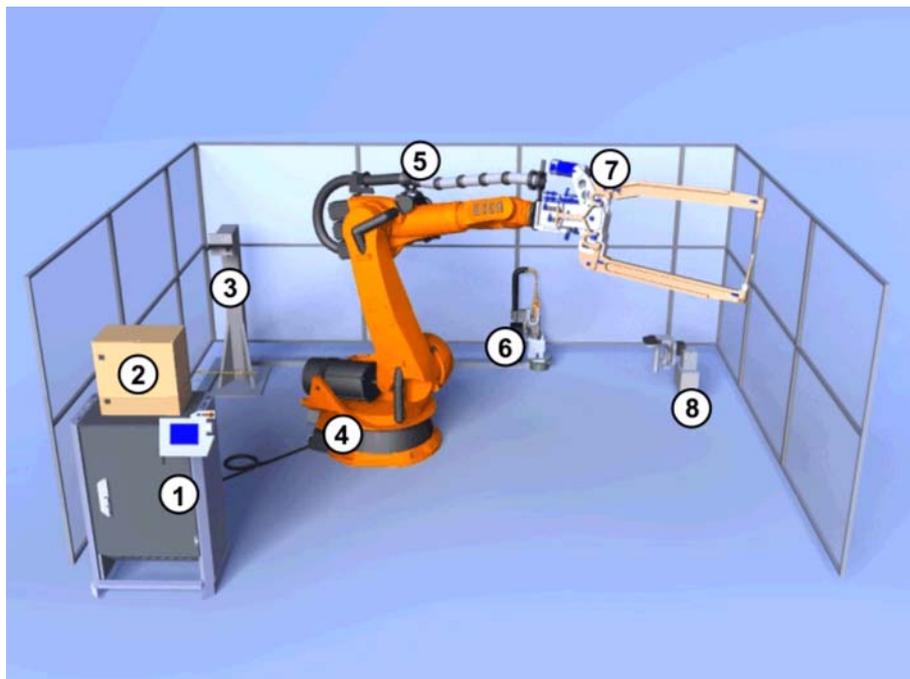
Vue d'ensemble d'une cellule de soudage
